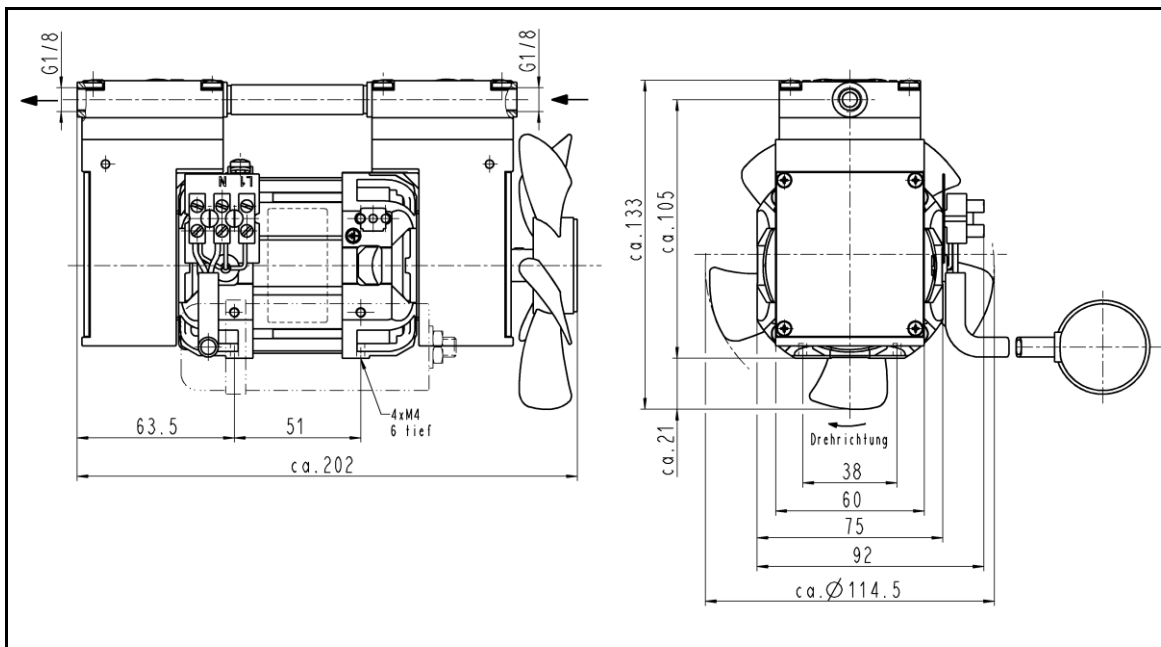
Befestigungsmaße Pumpe N 816.3 KPE
